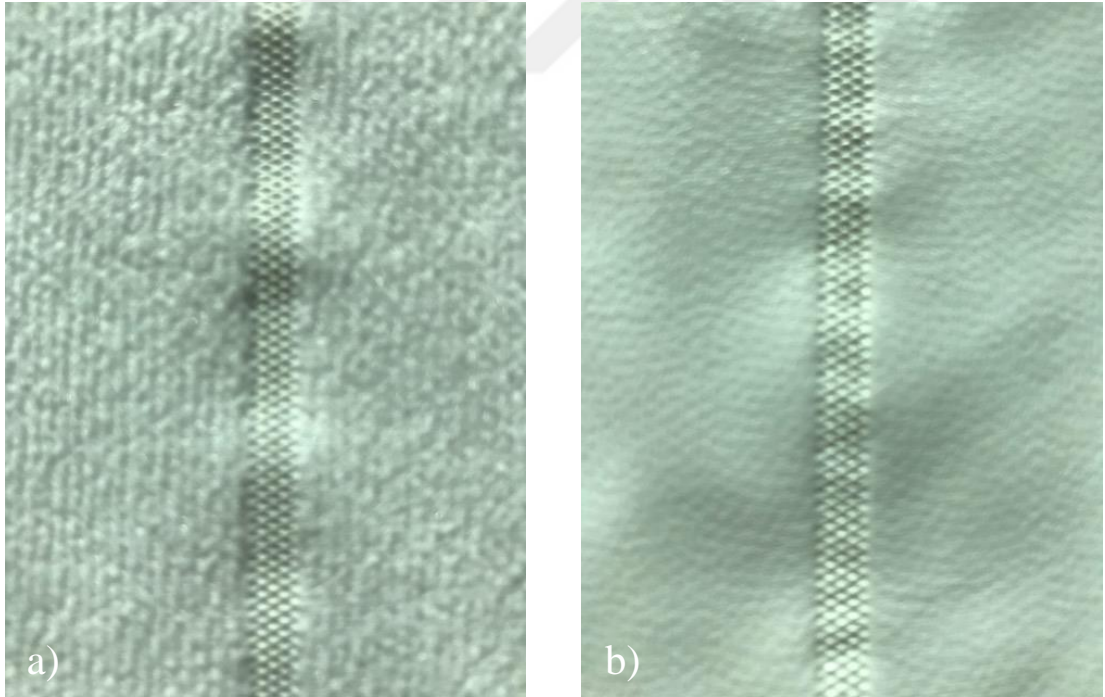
Ultrasonik dikiş makinesinde R1 ile dikilen O1 kumaşının görüntüsü
